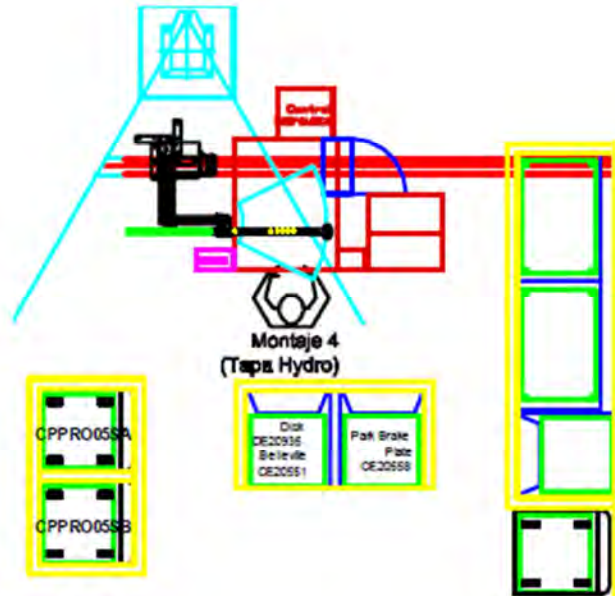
M LAYOUT DEL PREMONTAJE DEL FRENO DE APARCAMIENTO
